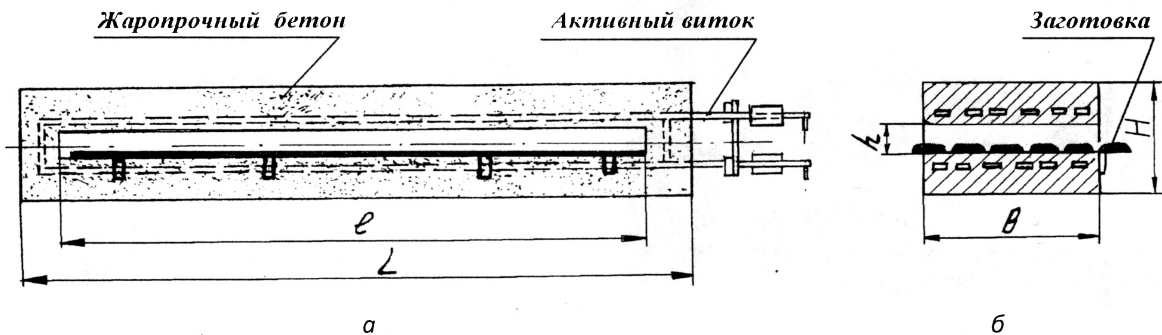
Индукторы для нагрева заготовок рессорных листов: а — под прокатку, б — под навивку
